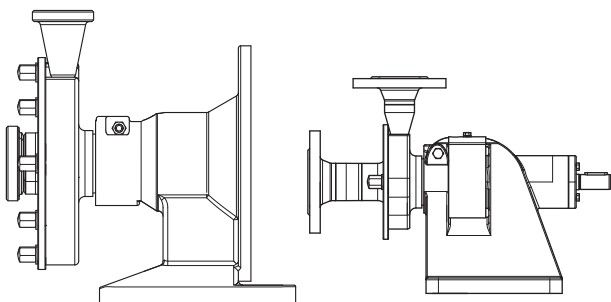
Máquina incompleta: bomba sin motor, acoplamiento y bastidor base, ejemplo basado en el tamaño constructivo KF y L
